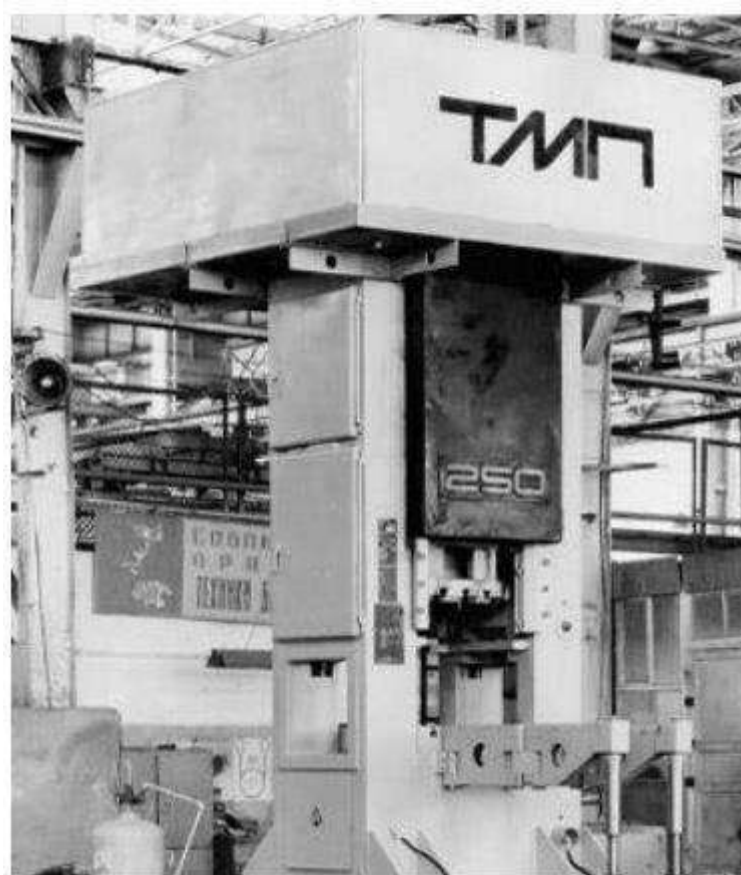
Загальний вигляд верстата КЖ2534
